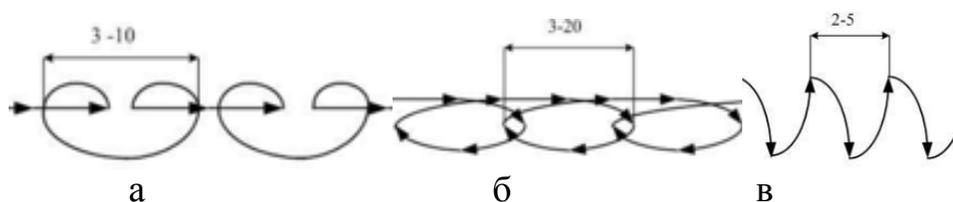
Схема движения торца проволоки к основному металлу:
